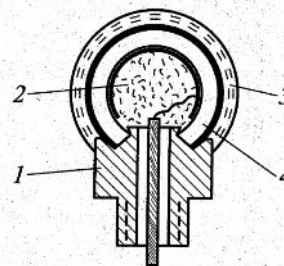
Конструкция гидрофона: 1-корпус; 2-касторовое масло; 3-резина; 4-пьезоэлемент
